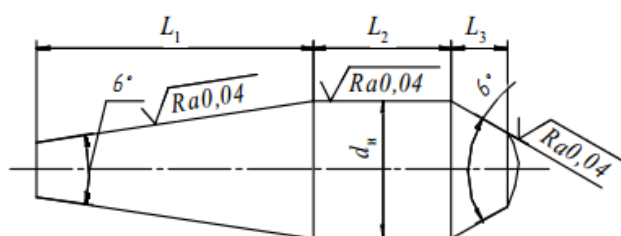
Твердосплавный дорн для обработки глубоких отверстий малого диаметра
